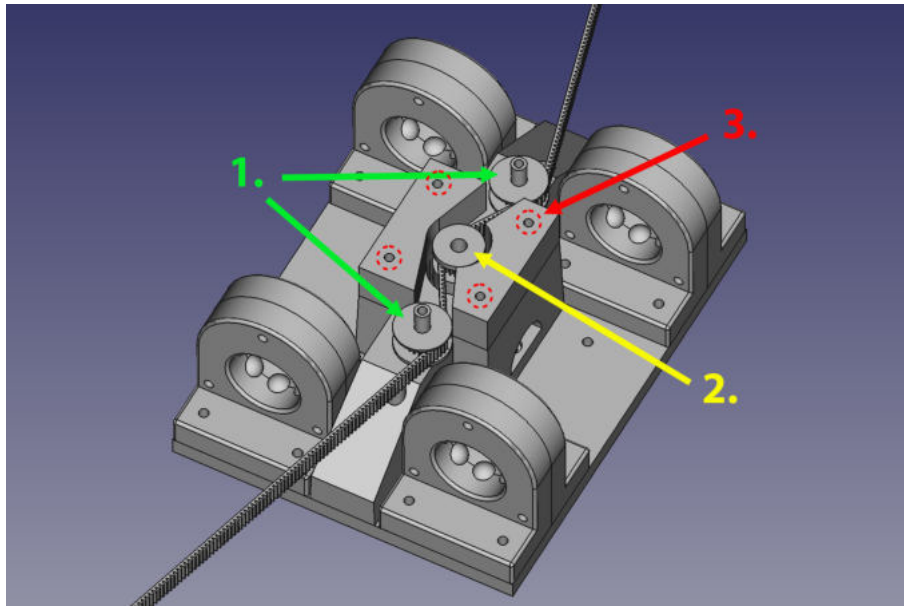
Slider-Motor Befestigung in der Mitte auf Slider-Plattform. Vier Befestigungen an Aluminiumrohren. Zwei Umlenkrollen (1.) um Zahnriemen gegen Zahnrad am Motor zu drücken (2.).
